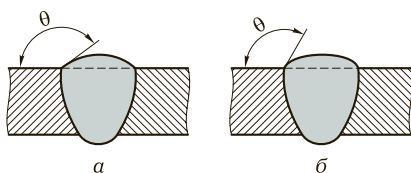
Избыточные выпуклости корня шва углового и стыкового сварных соединений:
